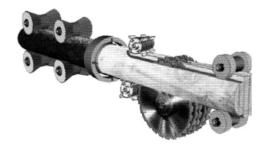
Схема работы фрезерно-профилирующего агрегата
